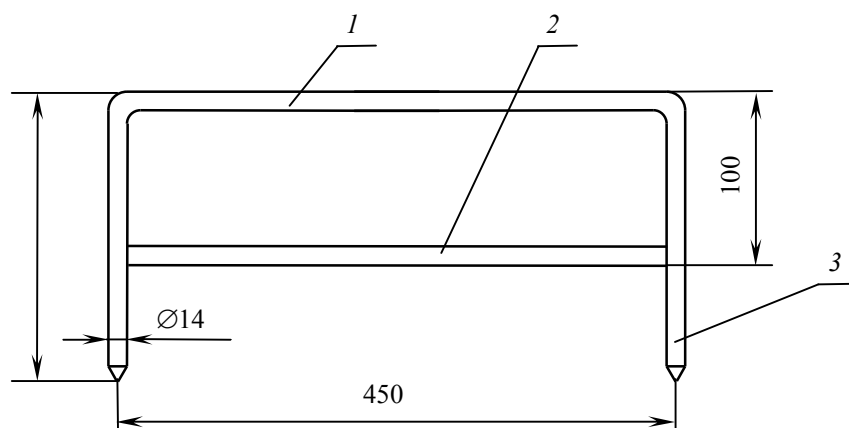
Опора к приспособлению для определения усилия отгиба пучка побегов:
